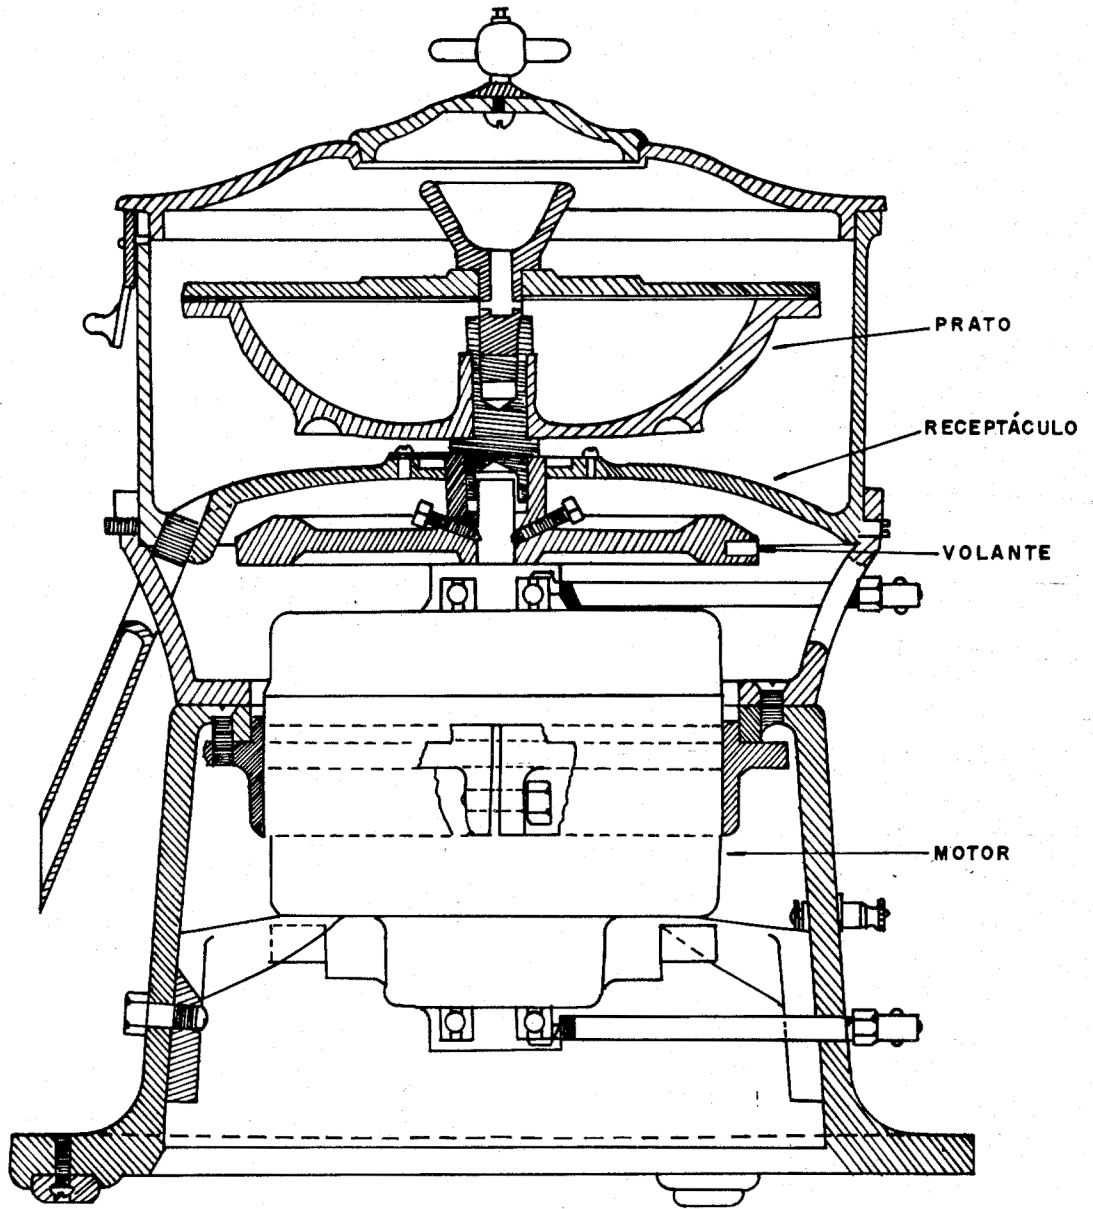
APARELHO PARA EXTRAÇÃO DE BETUMES
